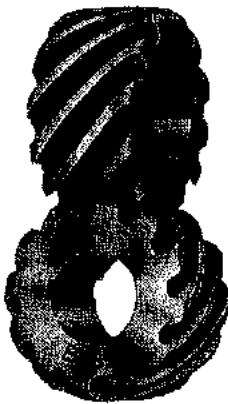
Engranaje helicoidal con ejes cruzados (Boston Gear Works)
